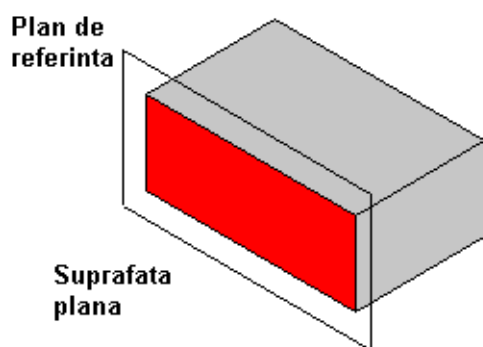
Plan de referință definit printr-o suprafață plană
